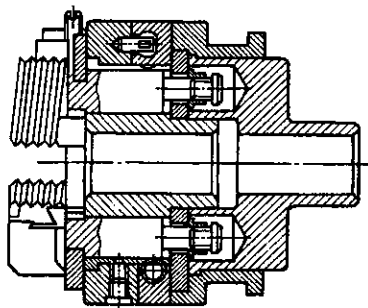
Резьбонарезные самооткрывающиеся головки с тангенциальными плоскими гребенками
